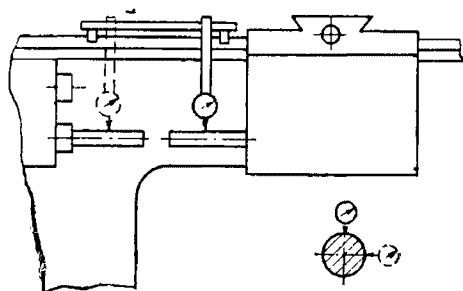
Схема замера соосности отверстий коробки подачи и фартука
